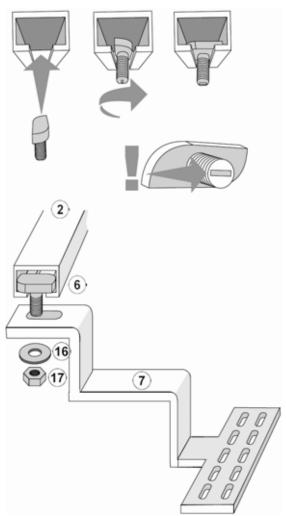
Hammerkopfschraube in das C-Profil einführen und bis zum Anschlag drehen. Durch die Kerbe am Gewindeende kann die korrekte Position der Schraube überprüft werden bzw. mit Hilfe des Schraubendrehers in die richtige Position gebracht werden.
